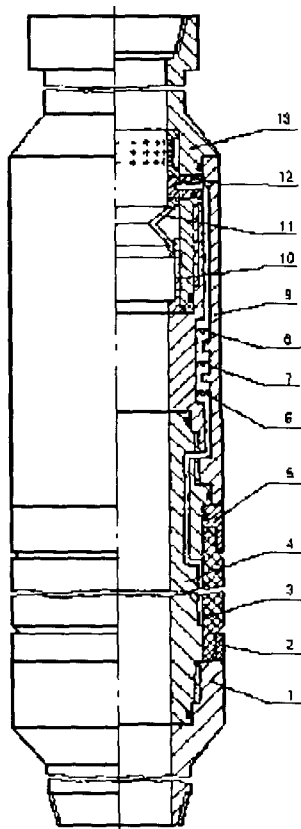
Пакер проходной гидравлический универсальный за колонный типа ППГУ
